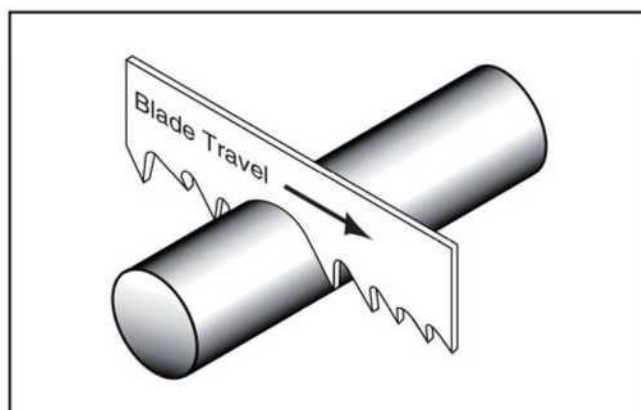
Зубья ленточного полотна, обращенные к заготовке.
